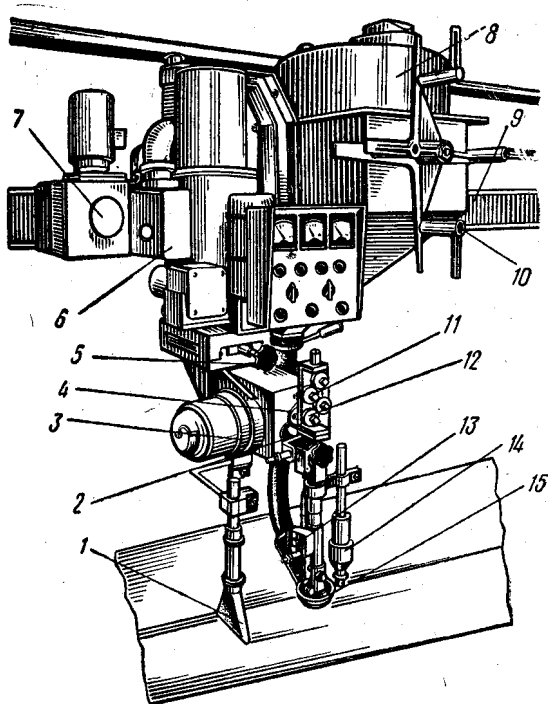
Автомат для электродуговой сварки:
